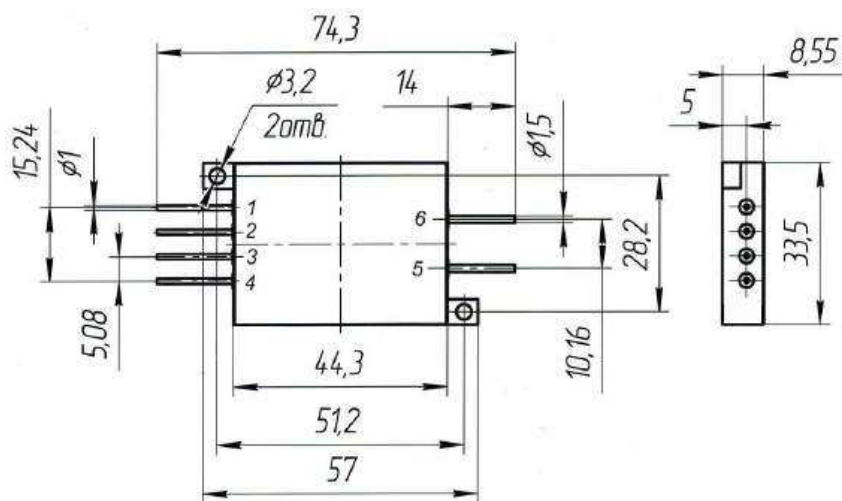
Габаритный чертеж микросборки 2609КВ014
